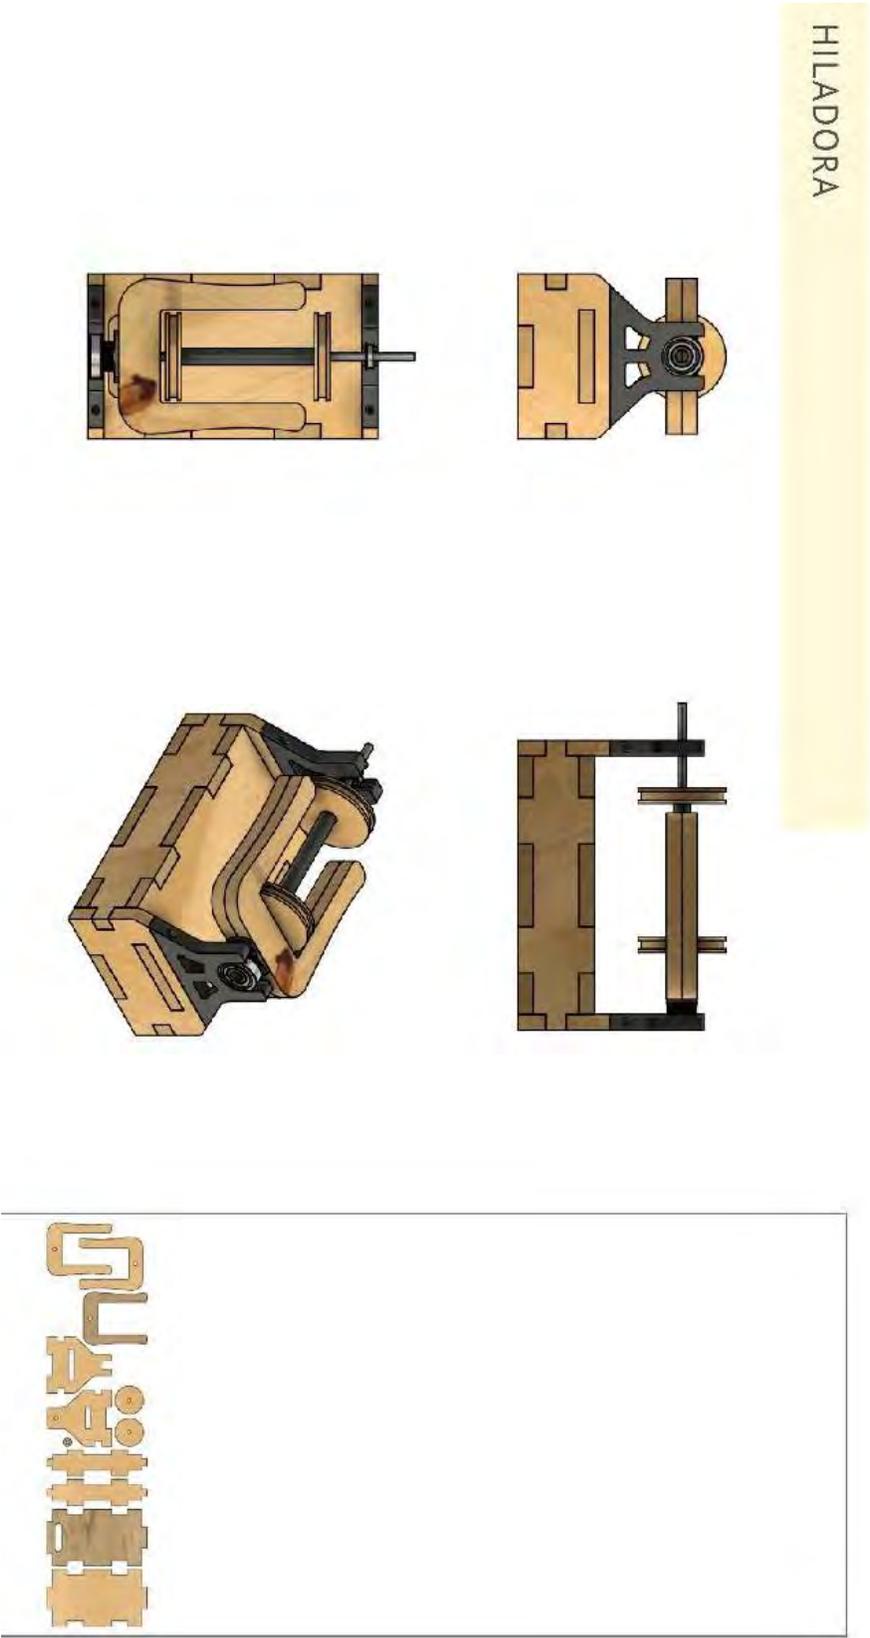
Vistas de las Máquina Hiladora y Plano Digital
